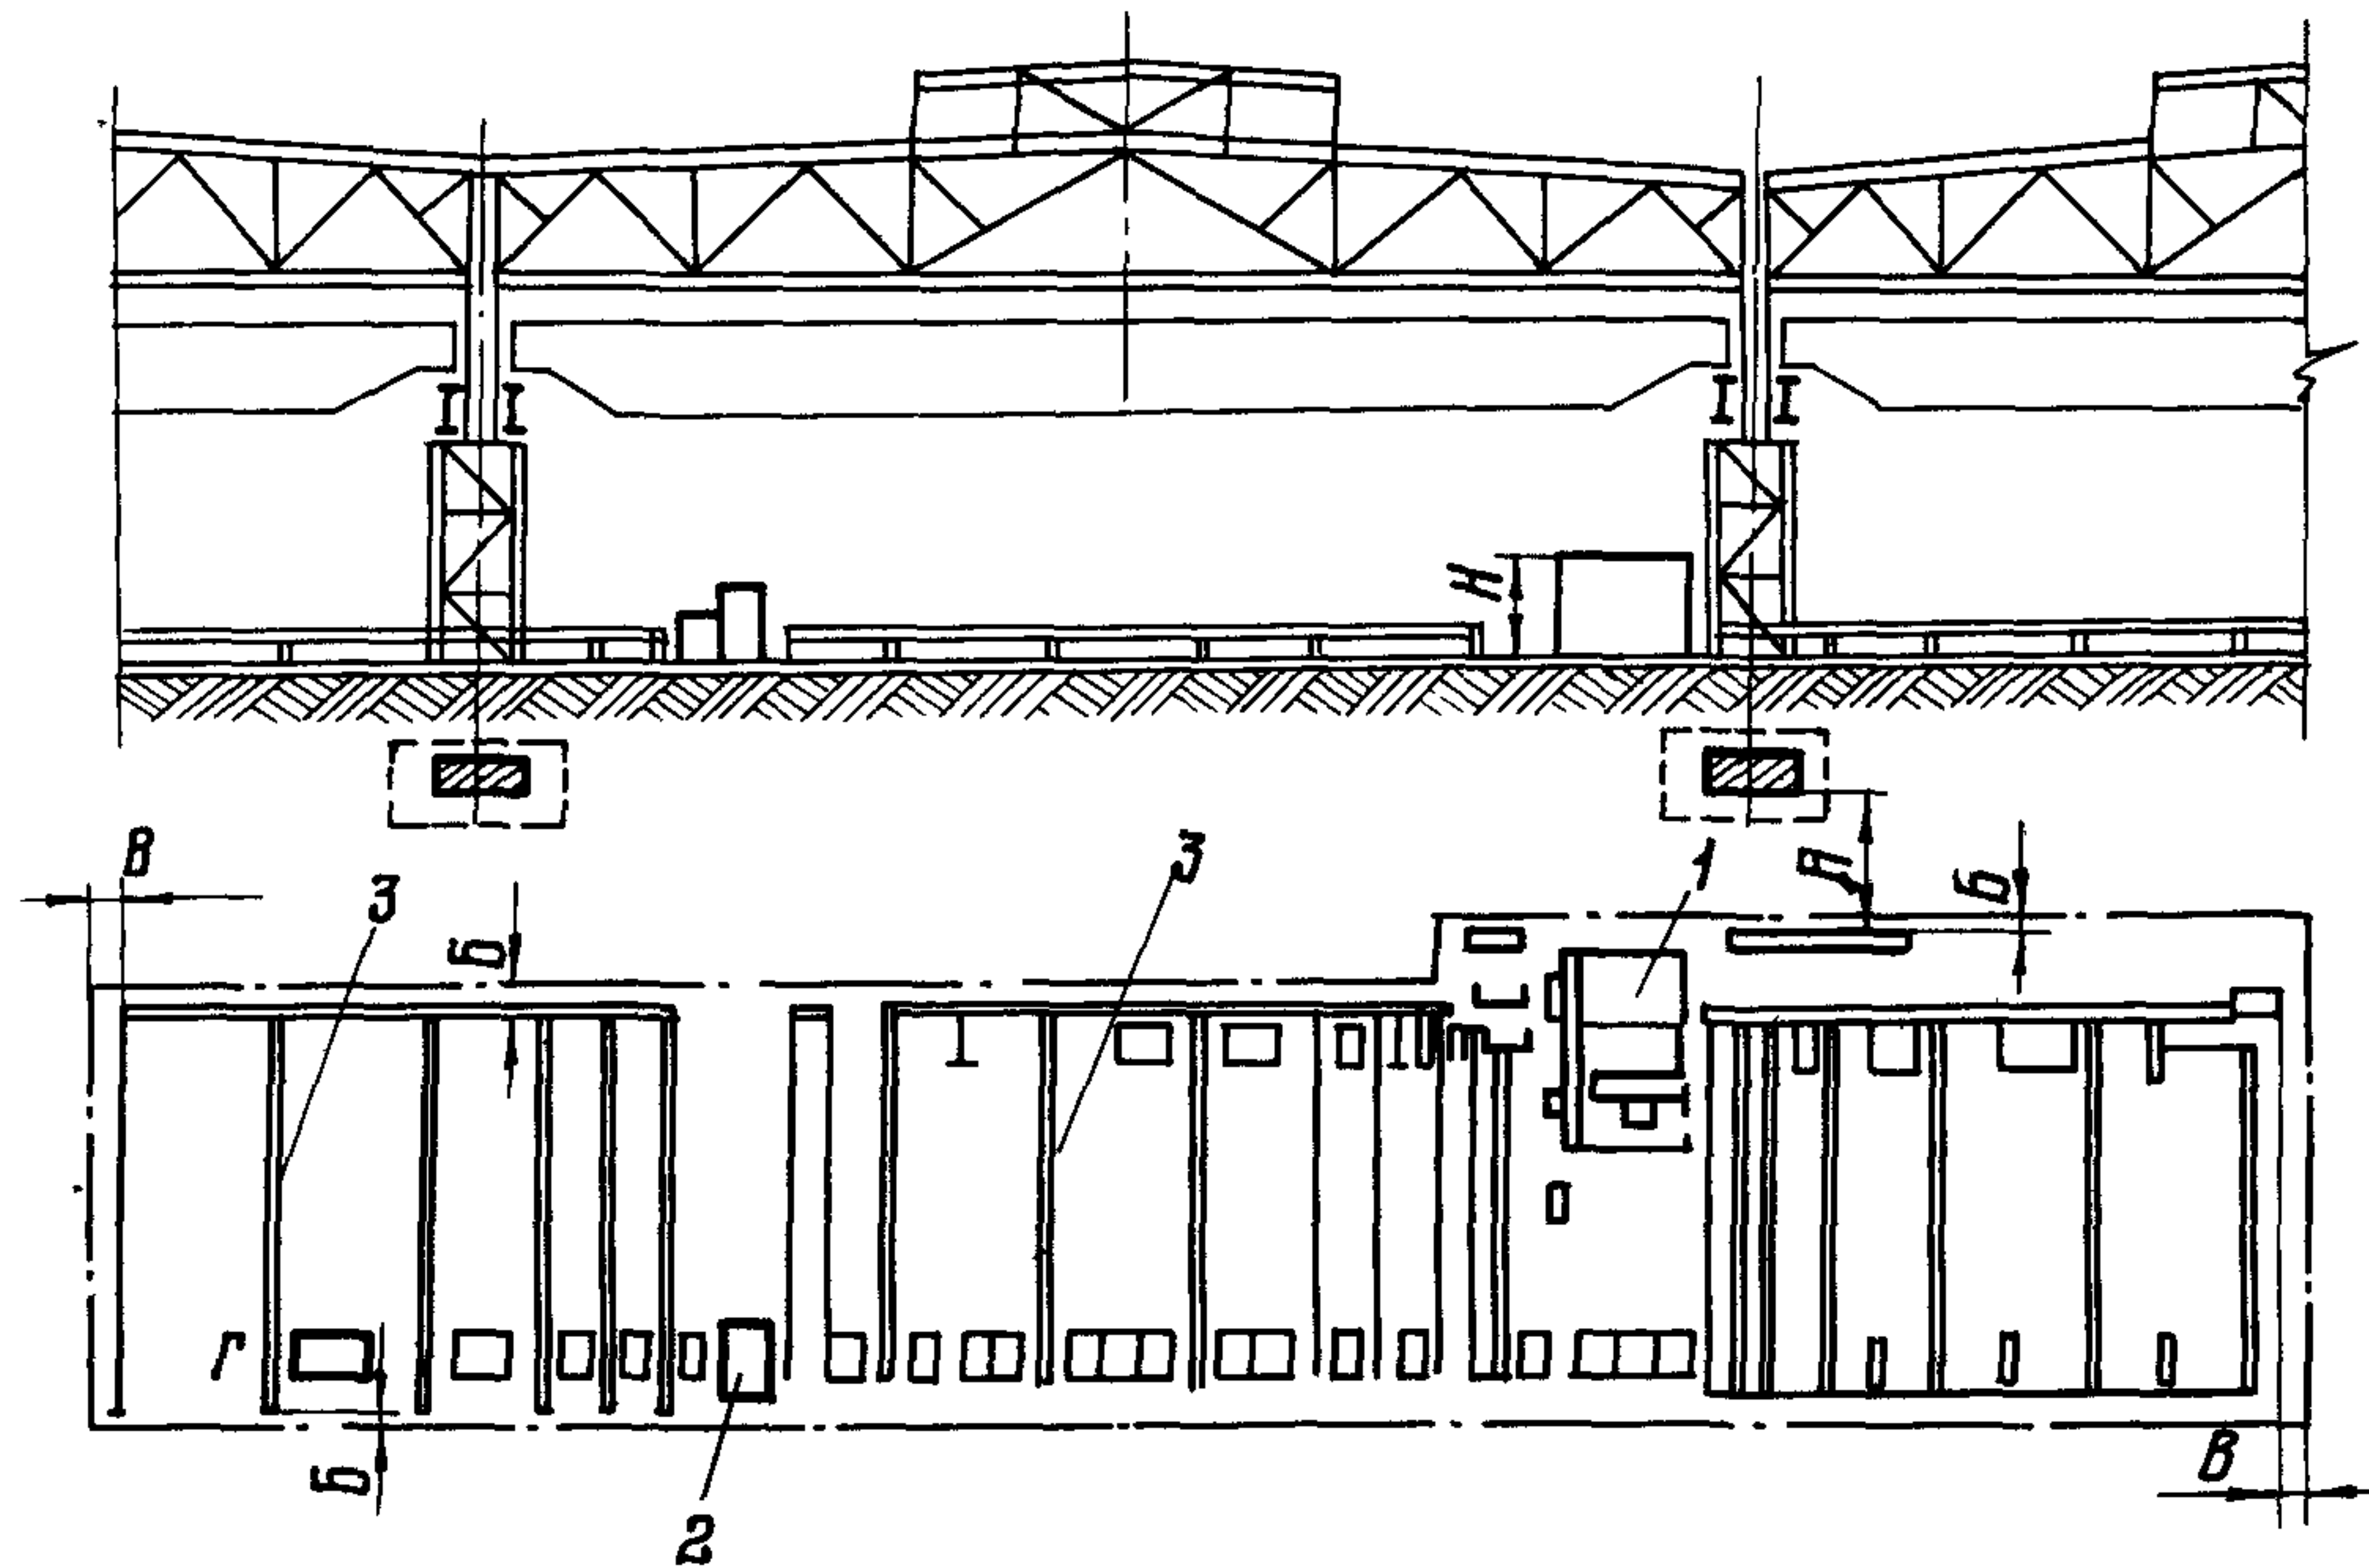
Размещение поточной линии для резки и сверления отверстий фирмы "Вагнер":
